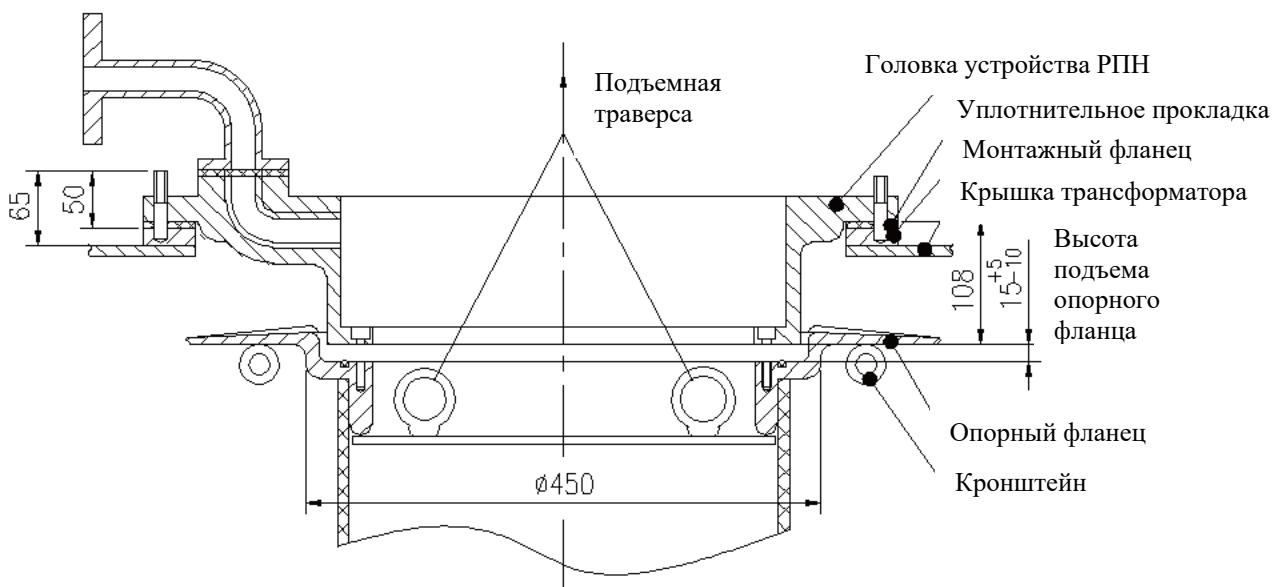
Установка устройства РПН в бак трансформатора колокольного типа
